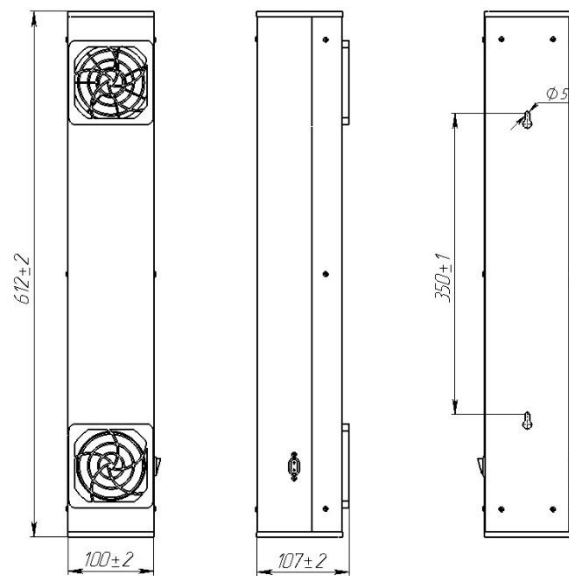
Общий вид, габаритные и присоединительные размеры облучателей
